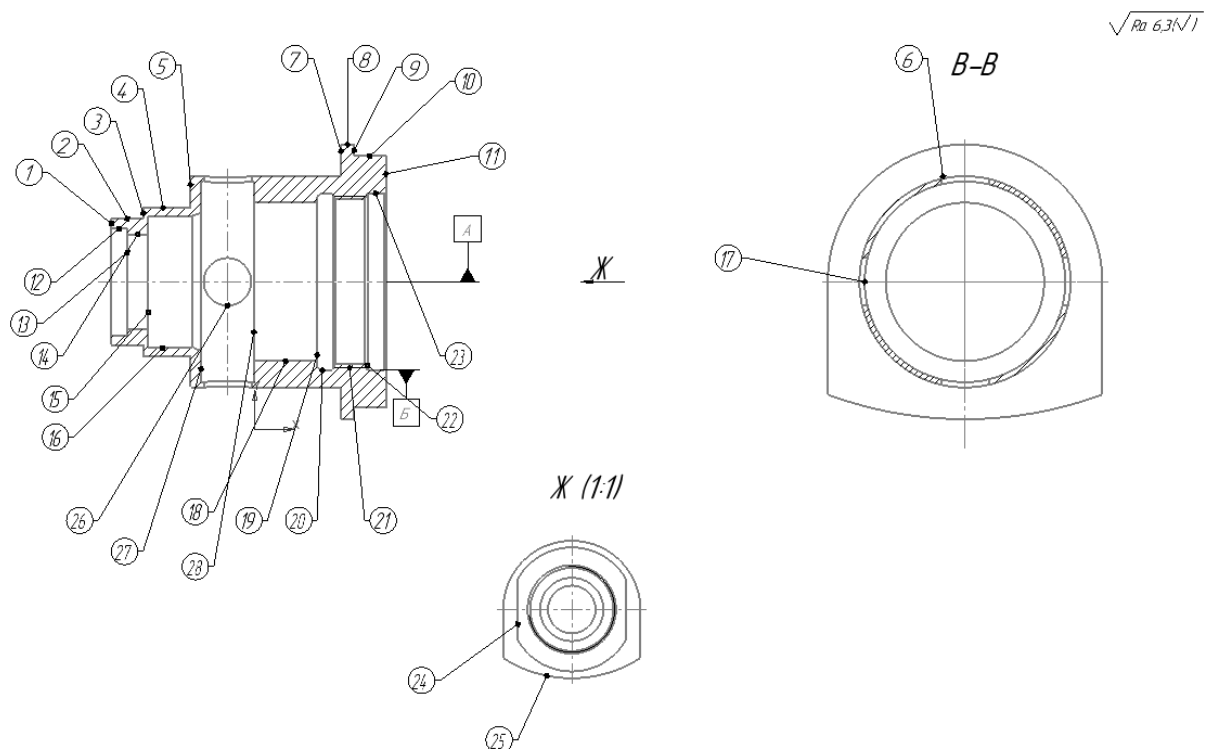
Деталь «корпус» з технологічної розміткою поверхонь
